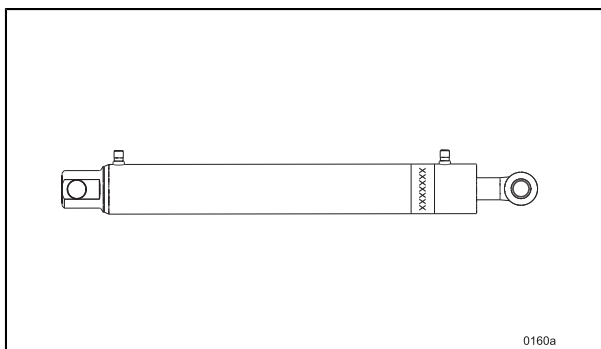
Kennzeichnung von Komponenten wie z.B. Zylindern.
